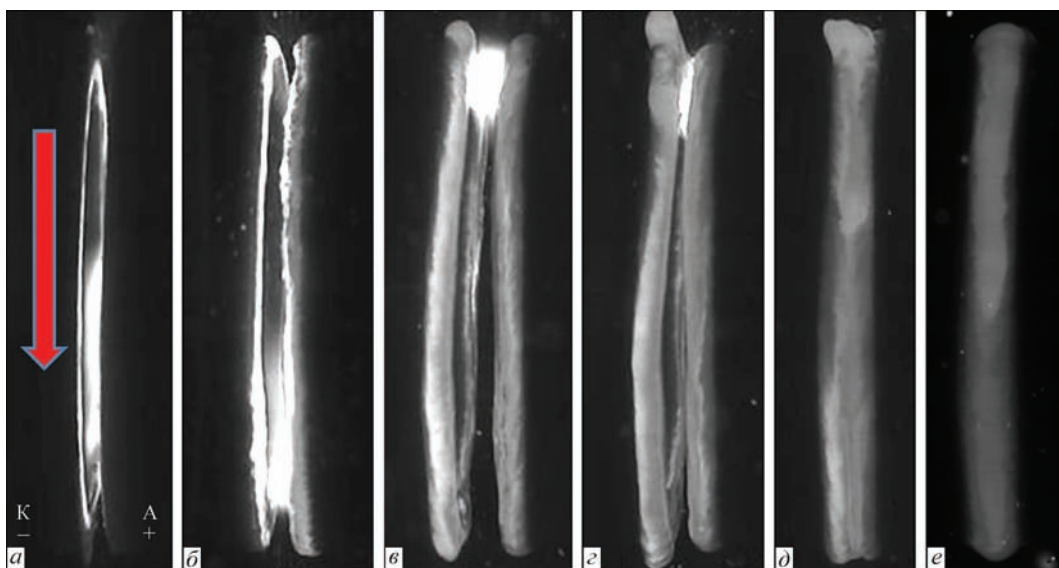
Стадии ПСМД труб: а — начало перемещения дуги под действием УМП; б — формирование слоя расплава на торцах труб; в — перемещение расплава в процессе нагрева; г — обновление расплава перед осадкой; д — начало осадки; е — формирование сварного соединения
